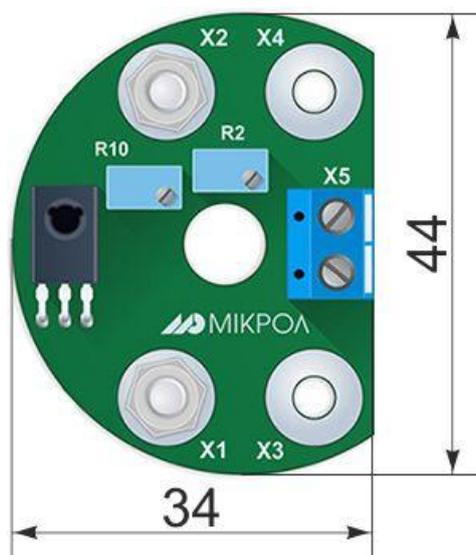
Внешний вид и габаритные размеры БПО-530
